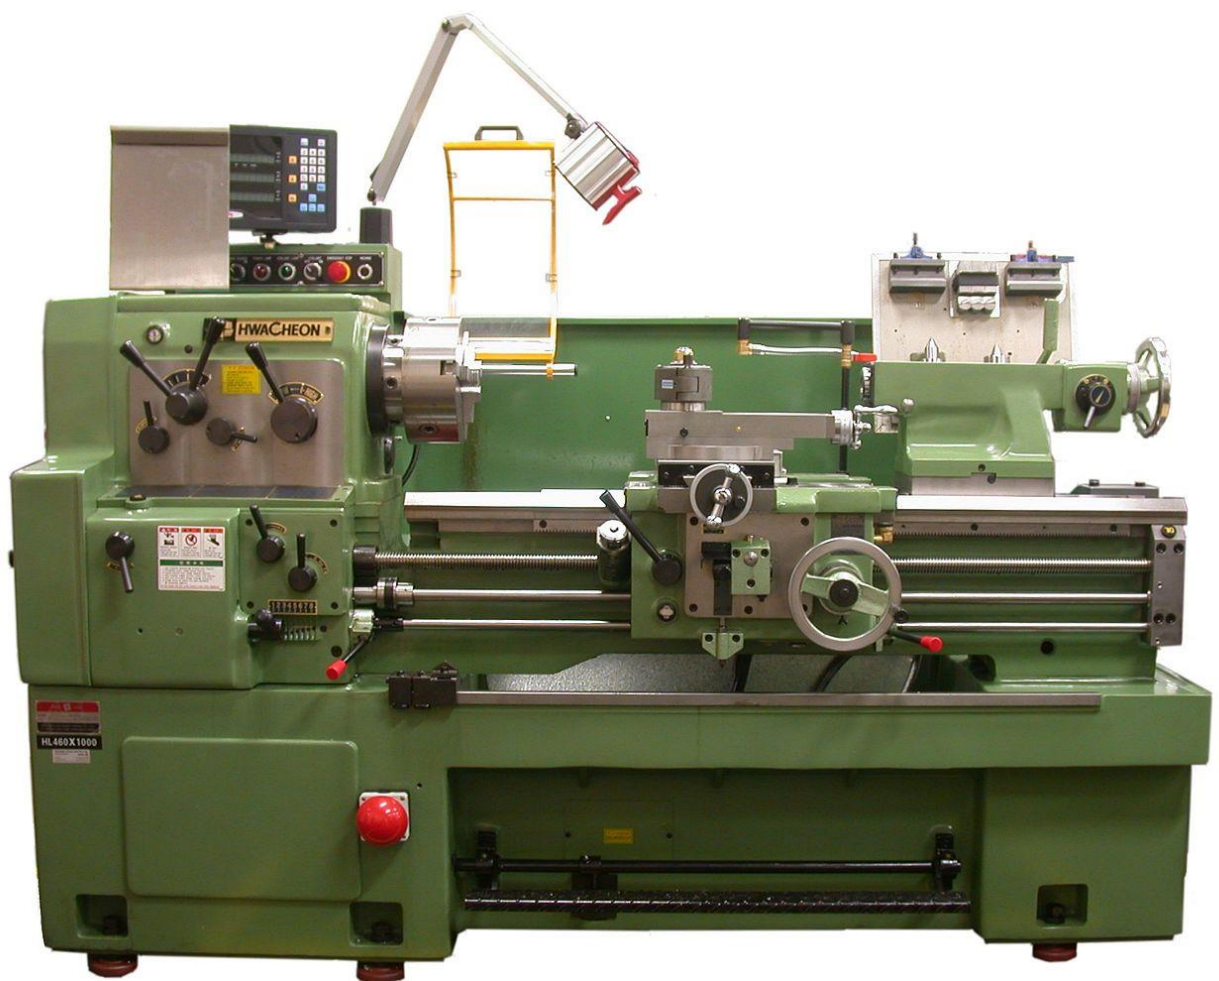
Універсальний токарно-гвинторізний верстат
